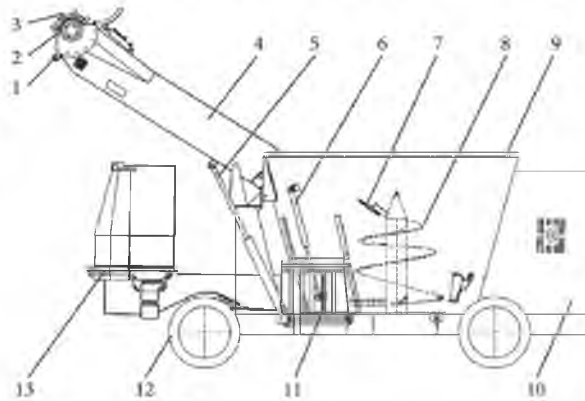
Конструкція самохідного кормозмішувача: 1 – опорне колесо; 2 – ролик; 3 – різець; 4 – конвеєр; 5 – підйомний гідроциліндр; 6 – нагнітальний гідроциліндр; 7 – рухома лопатка; 8 – шнек; 9 – бункер; 10 – блок дизельного двигуна; 11 – розрядний пристрій; 12 – опорні колеса; 13 – кабіна.
